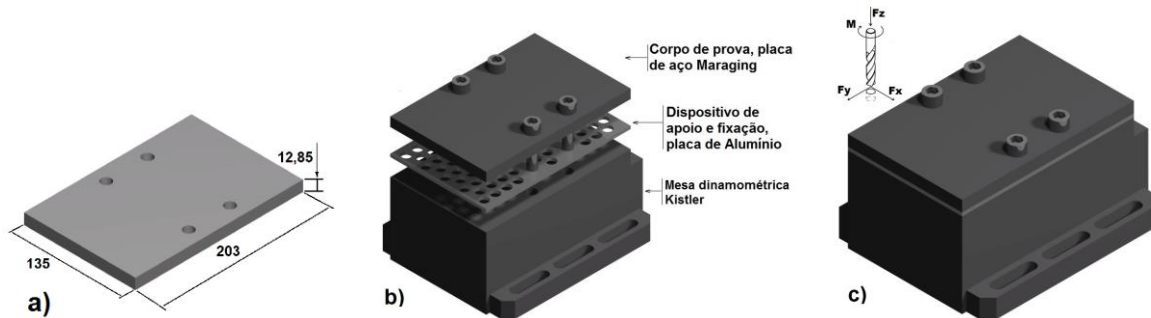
a) Corpo de prova; b) Montagem do dispositivo de apoio e fixação do corpo de prova; c) Corpo de prova montado para início do ensaio.
